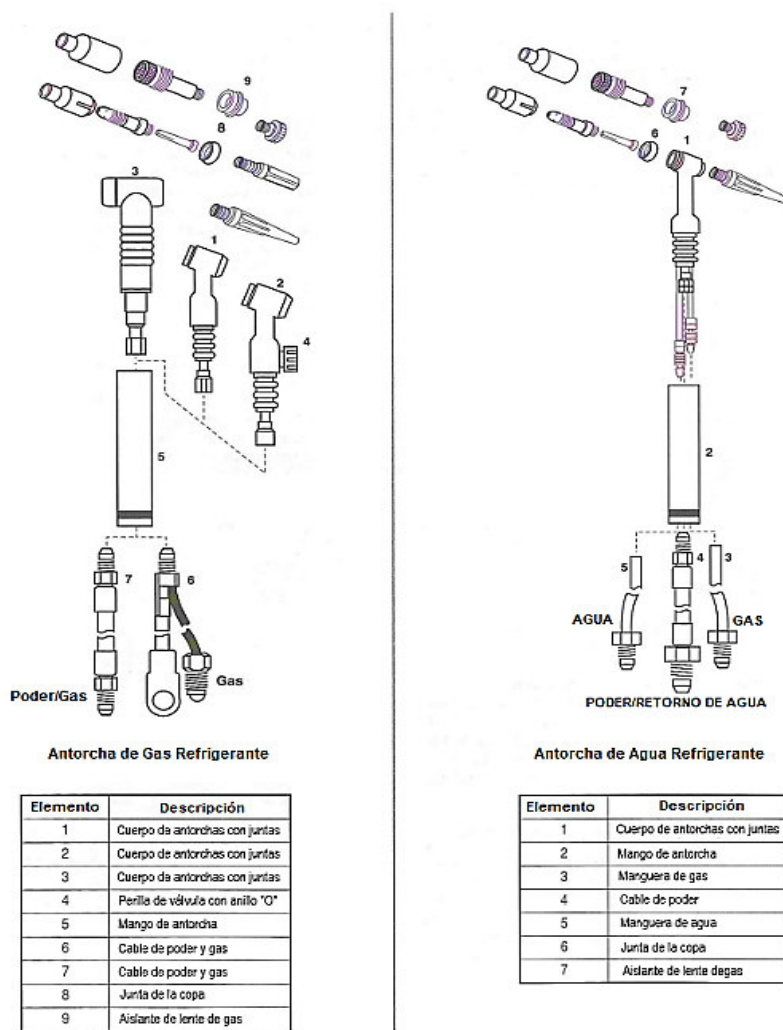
Antorchas típicas para soldadura GTAW. [10]
